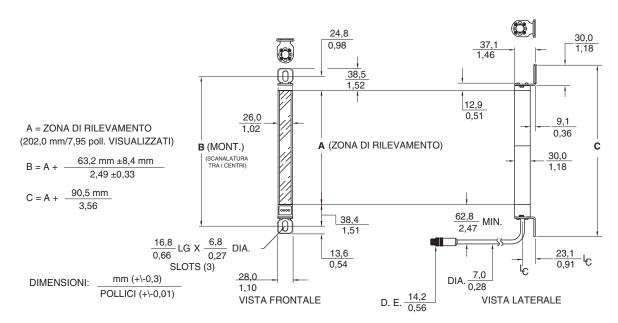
Dimensioni (Vedere Tabella 30 per le Dimensioni A, B e C)
